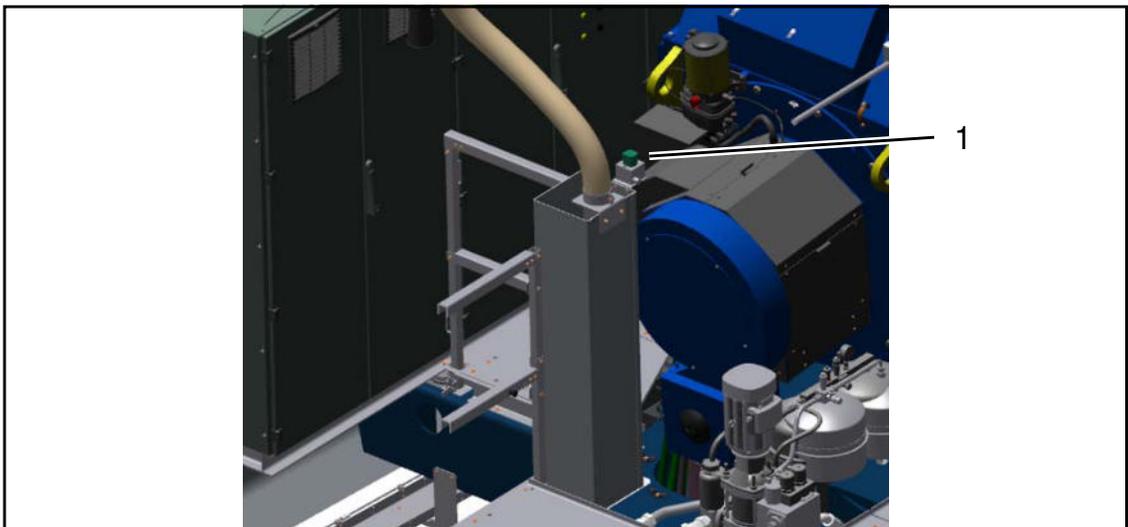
Ausschalter Mittelspannung (1) am Kettenkasten Elektrokettenzug
